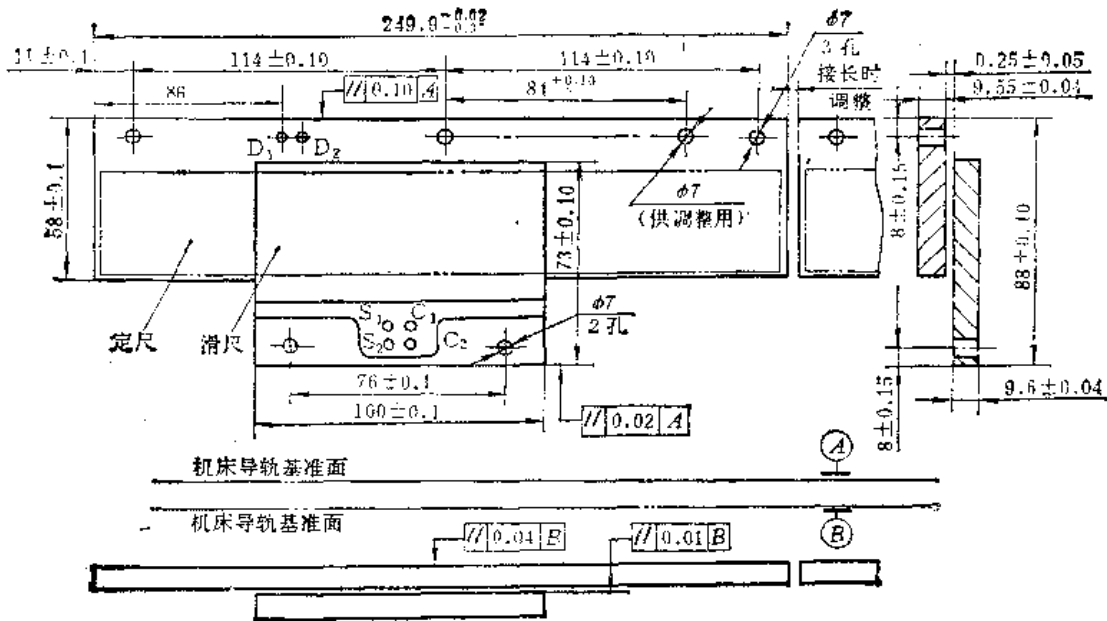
直线感应同步器外形尺寸, 安装尺寸和安装要求
